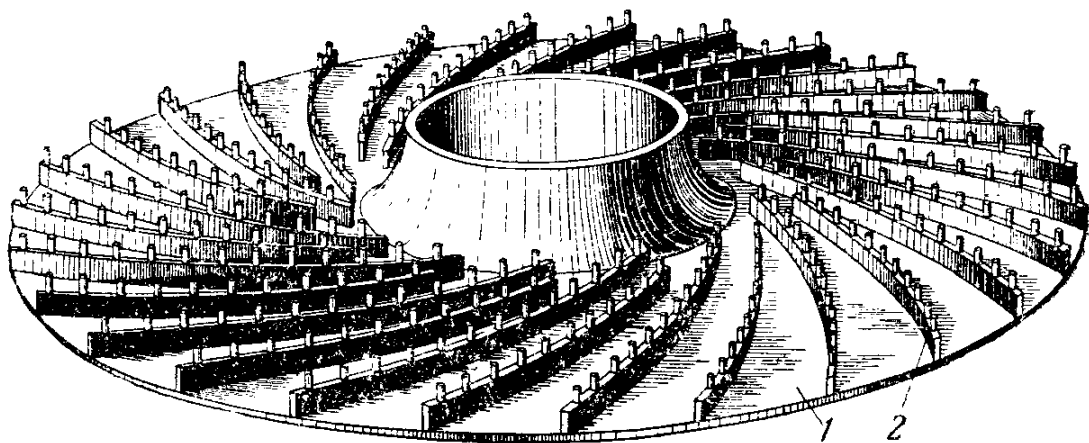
Рабочее колесо ротора турбокомпрессора:
